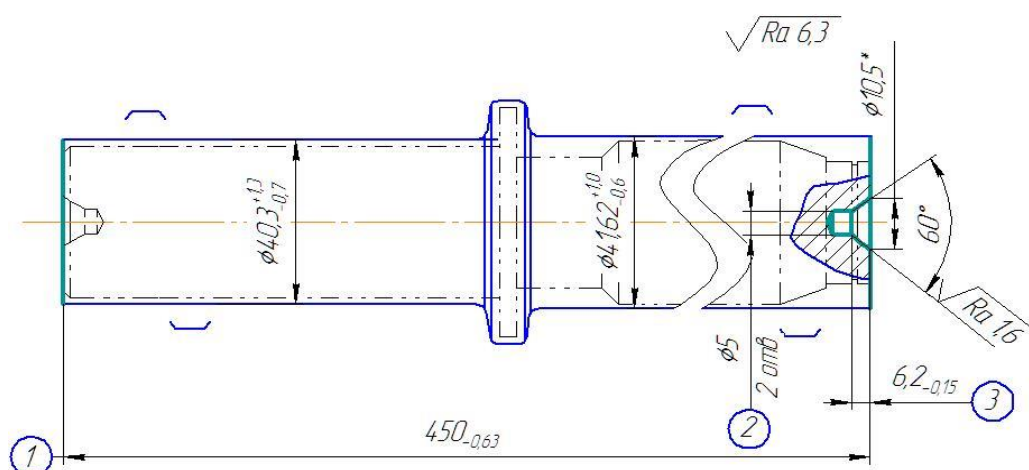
Закріплення заготовки в призмах на фрезерно-центрувальній операції
